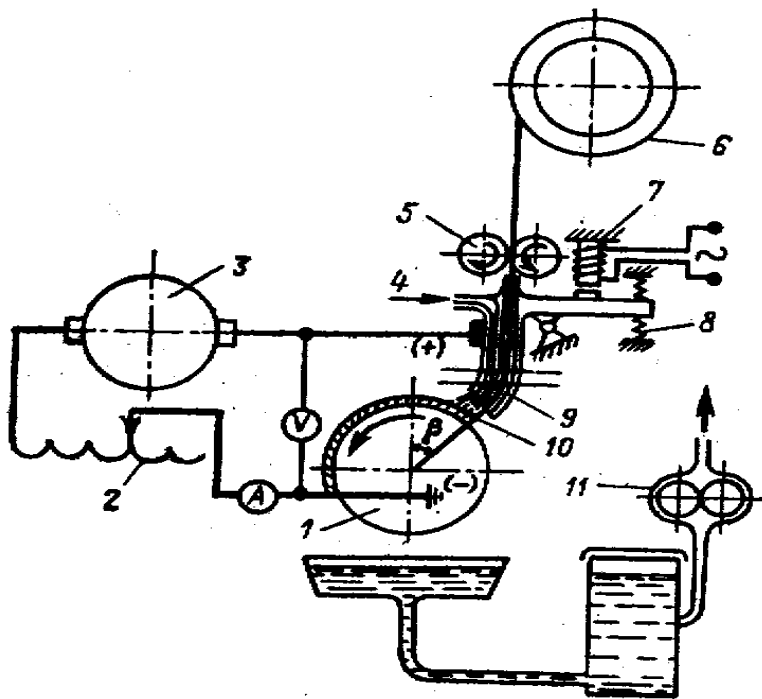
Електрокінематична схема установки для вібродугового наплавлення деталей
